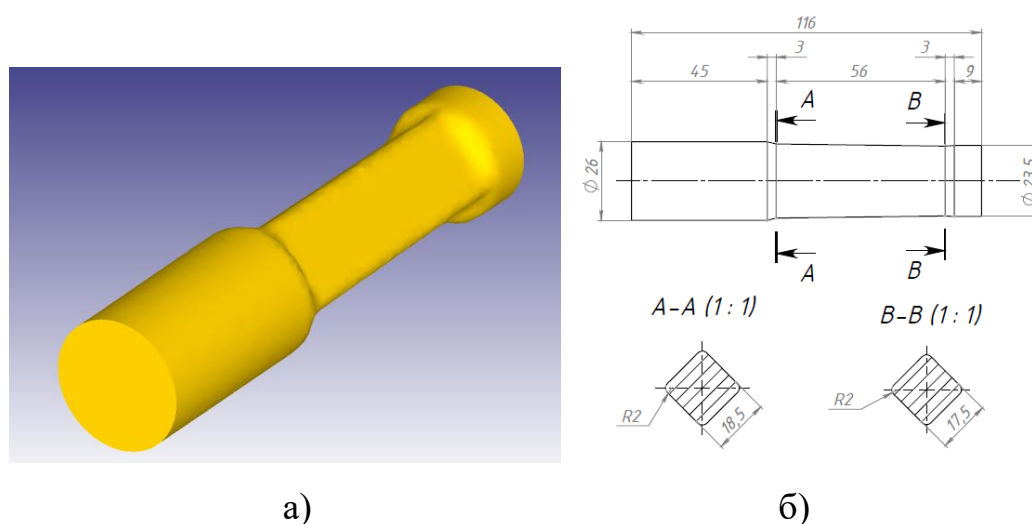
Профилированная заготовка под штамповочную вальцовку: а – трехмерное изображение; б – чертеж полуфабриката
